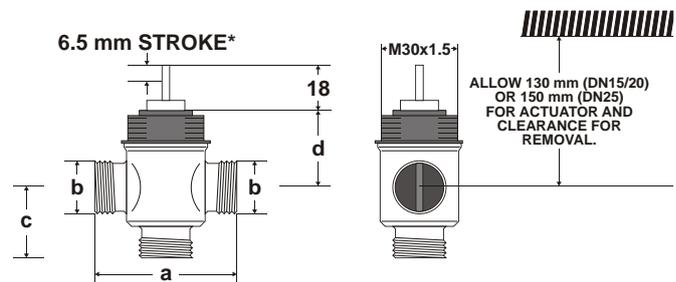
Válvulas de 3 vías, dimensiones (mm)
